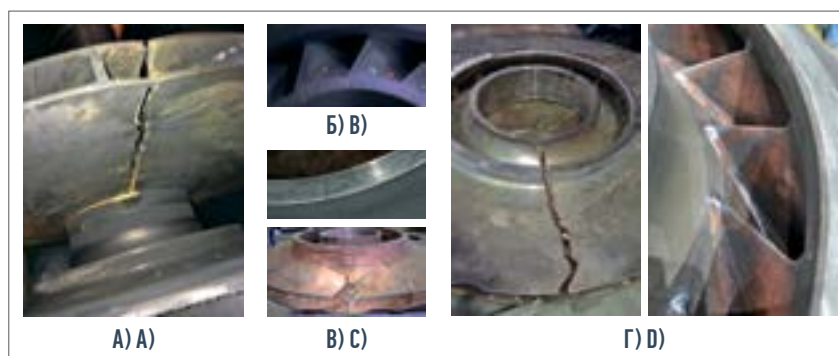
Повреждения колес 1–4-й ступеней компрессора:
